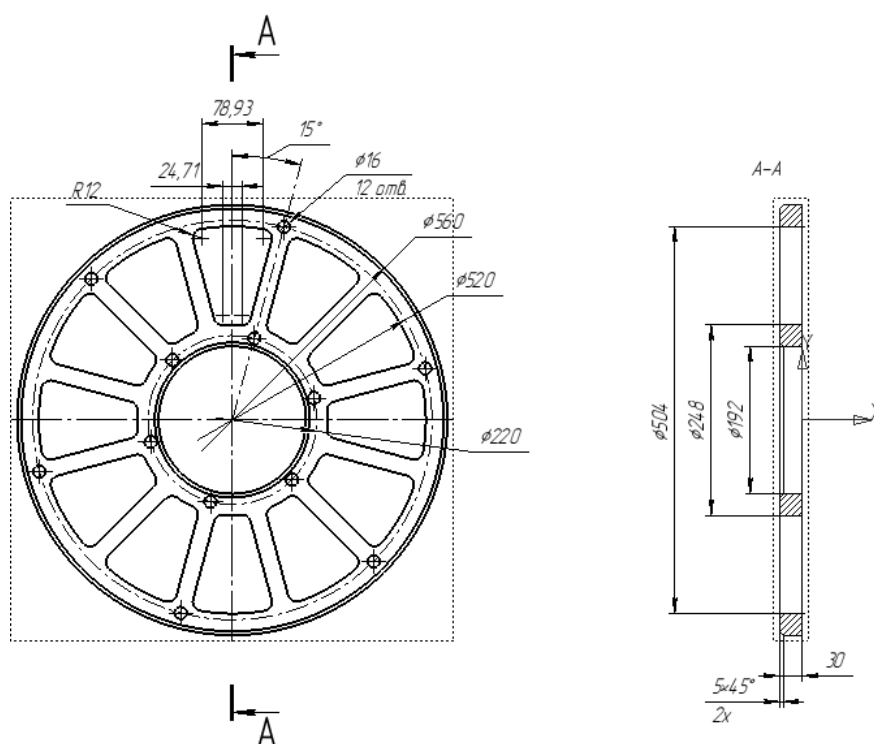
Ескіз робочої частини ячеювкої шайби
